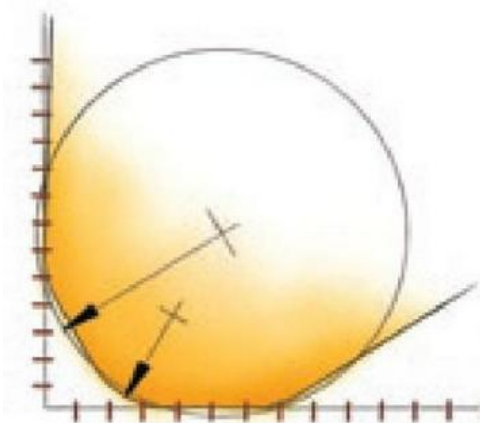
Схема вершины режущей части по технологии Wiper [6]
